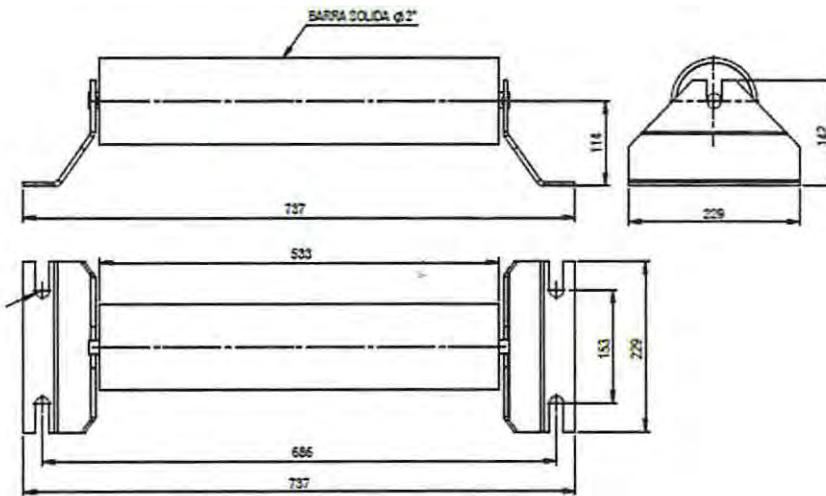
Leyton, E. (2007). Plano polines porta cables.
